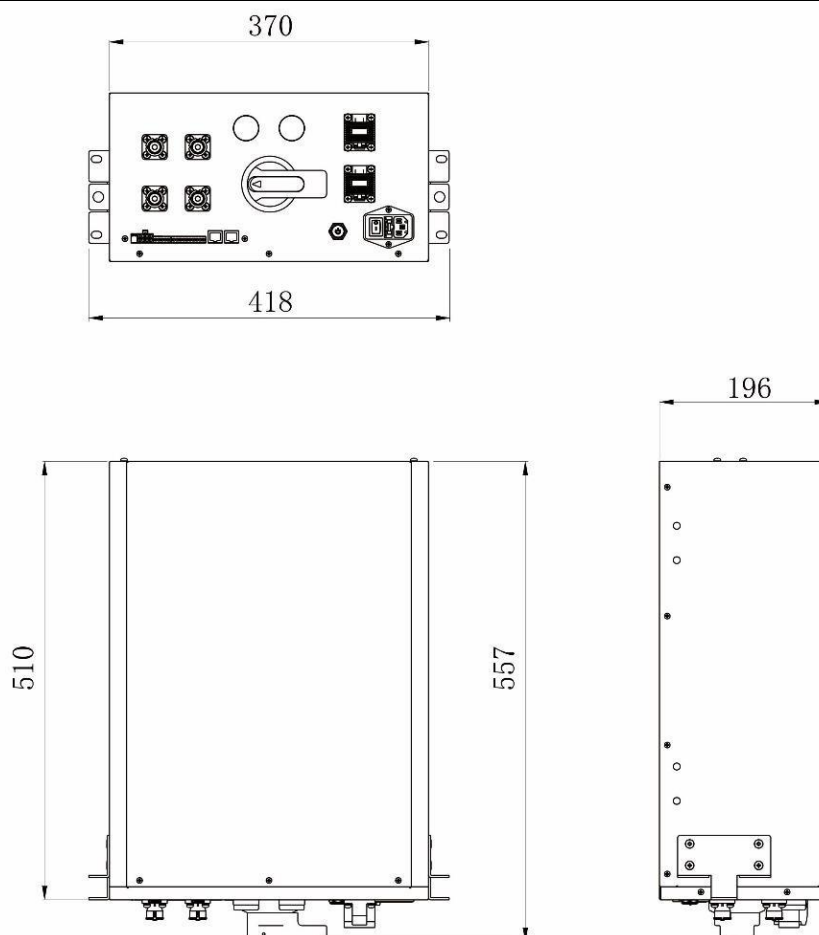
Dimensioni della scatola ad alta tensione (mm)
